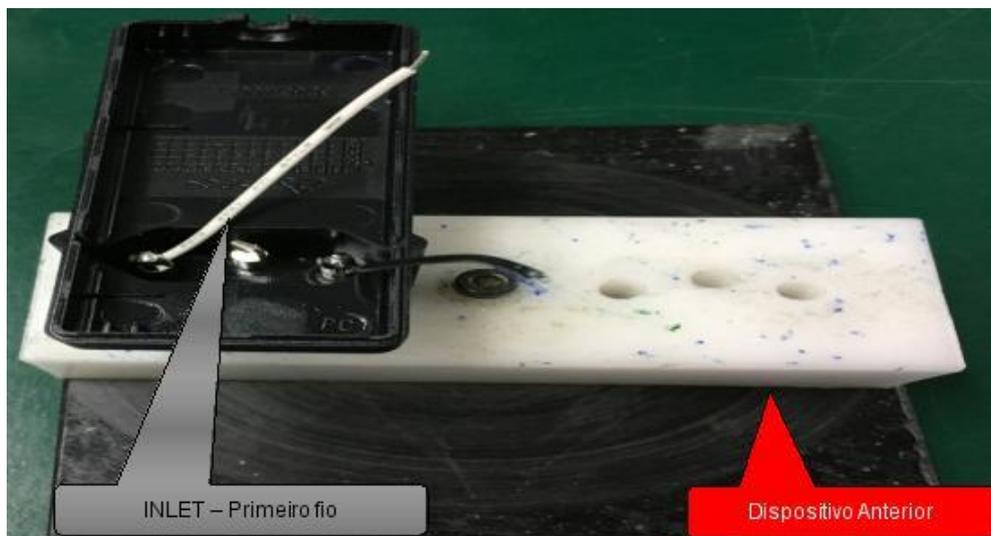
Dispositivo de Soldagem do Inlet (Antes) - Fonte: o próprio autor
